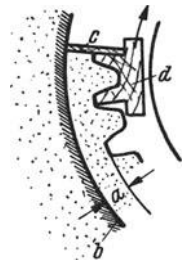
Aufstampfen der Zähne mit Zahnradformmaschine. *a* = Sandfüllung; *b* = schablonierter Durchmesser; *c* = Anschlagbrett; *d* = Zahnstück.
